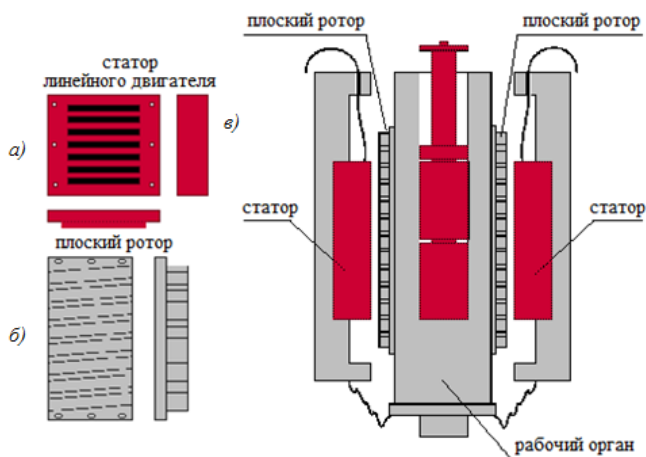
Конструкция статора и ротора линейного двигателя:
